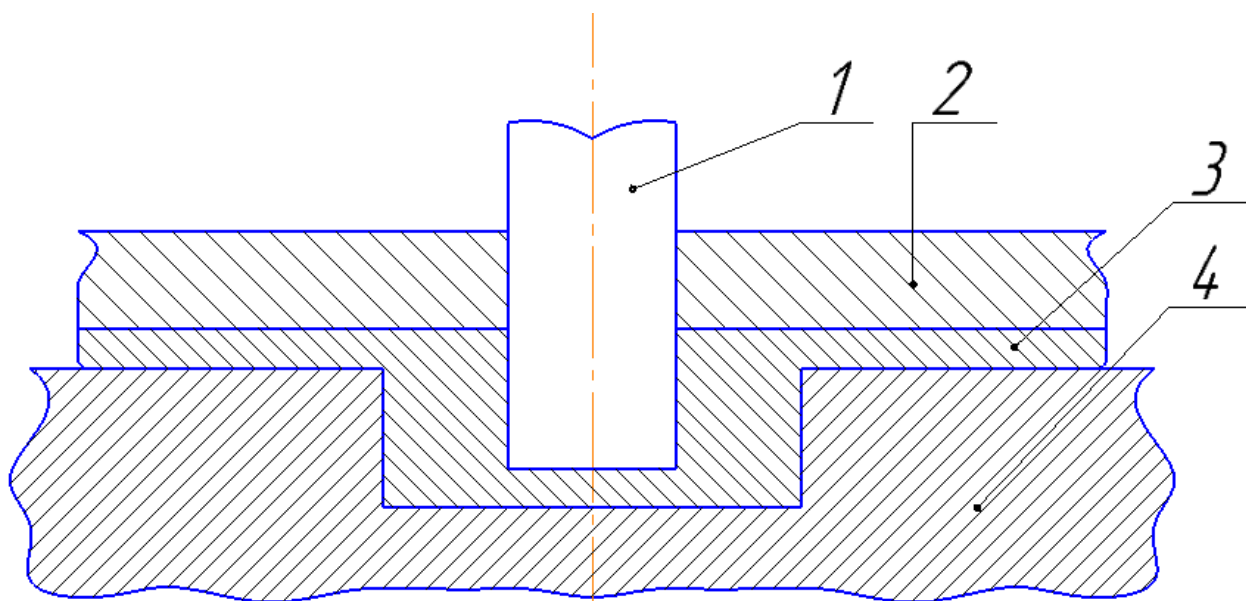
Холодная объемная штамповка в закрытом штампе [6]: 1 – пуансон; 2 – верхний штамп; 3 – тонколистовая заготовка; 4 – нижний штамп
